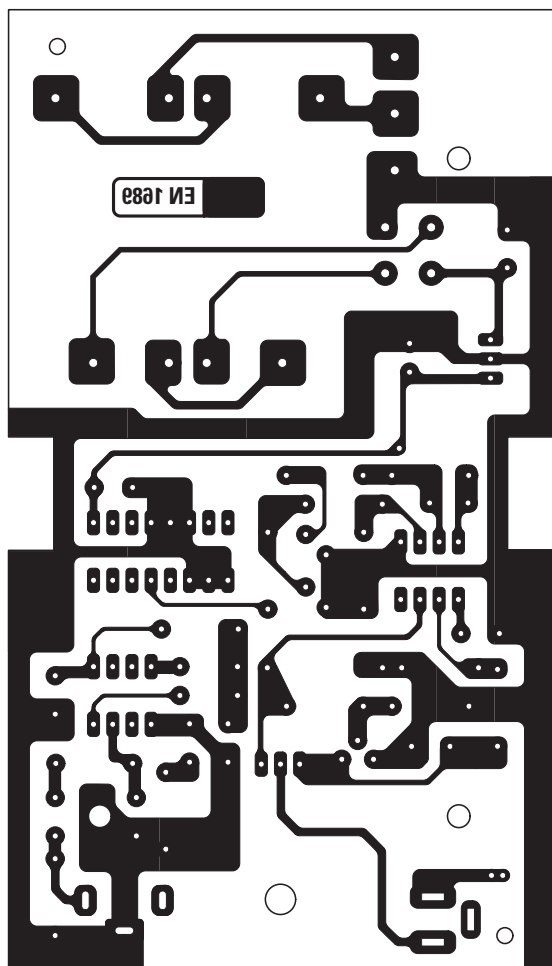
1 : Dessin, à l'échelle 1:1, du circuit imprimé double face à trous métallisés EN1689, côté soudures.
